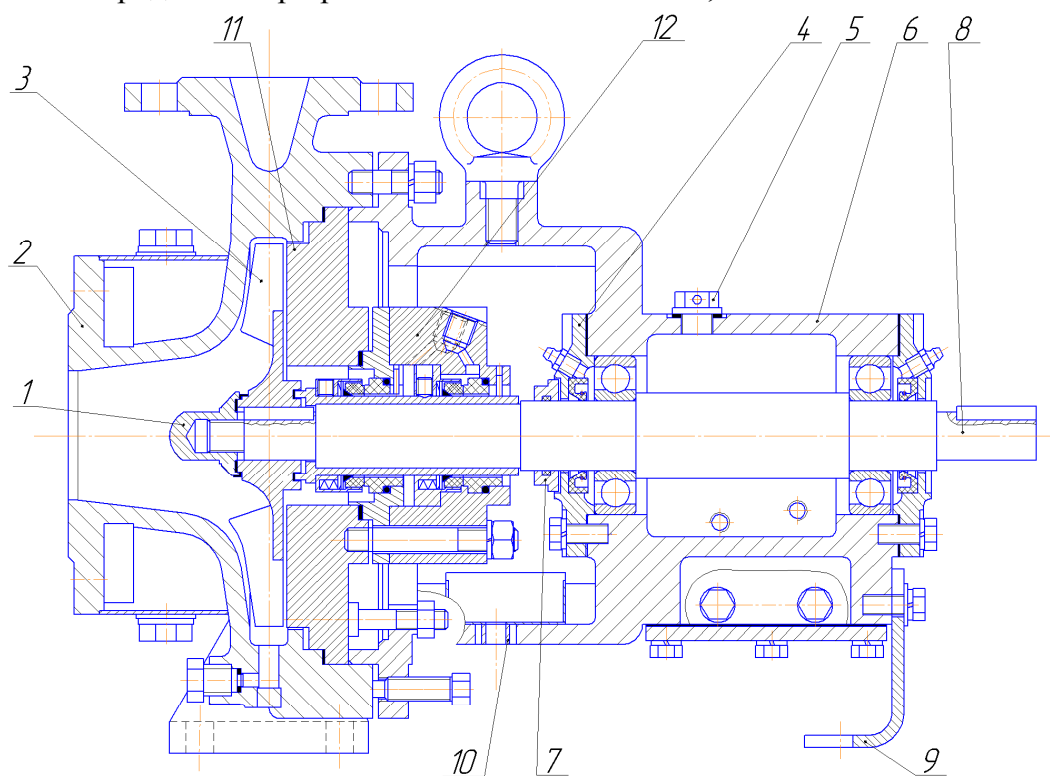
Продольный разрез насосов АХО40-25-160, АХО50-32-160, АХО50-32-200, АХО65-40-200, АХО125-80-250
